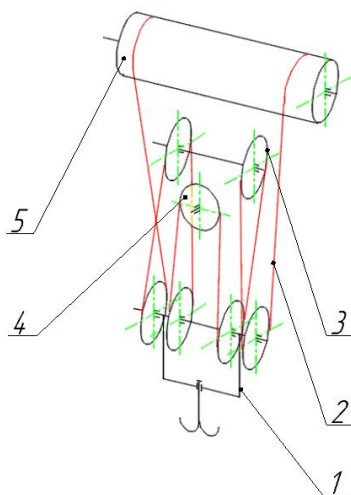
Кинематическая схема механизма подъема крановой установки
